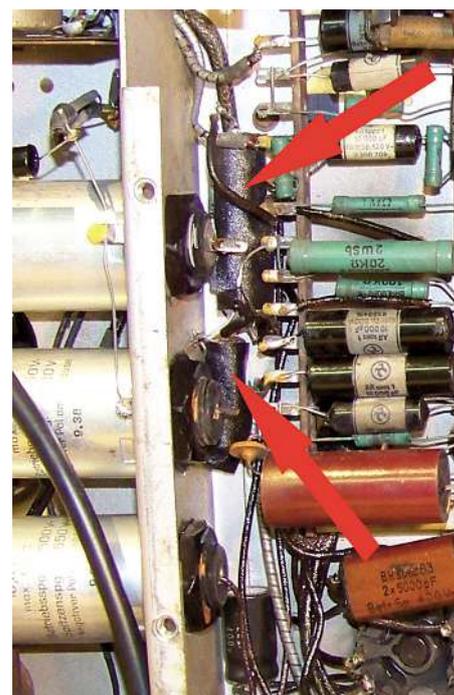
Detailaufnahme des Chassis mit (fast) unsichtbaren Ersatzkos
